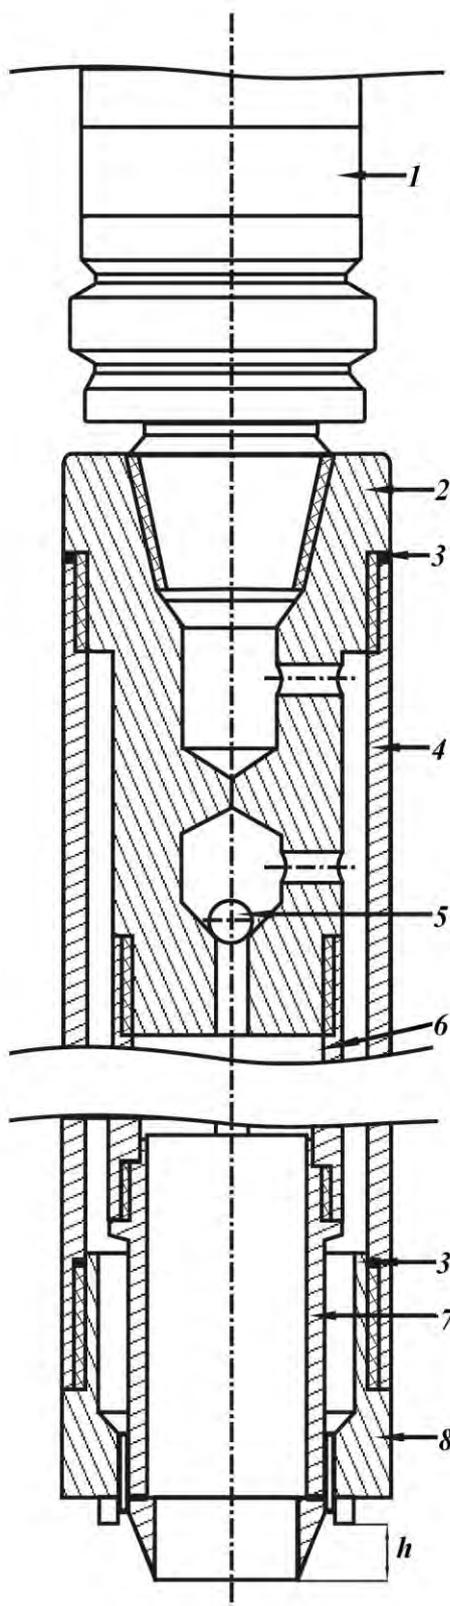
Предложенная конструкция забойной компоновки для прорезки угольных пластов:
